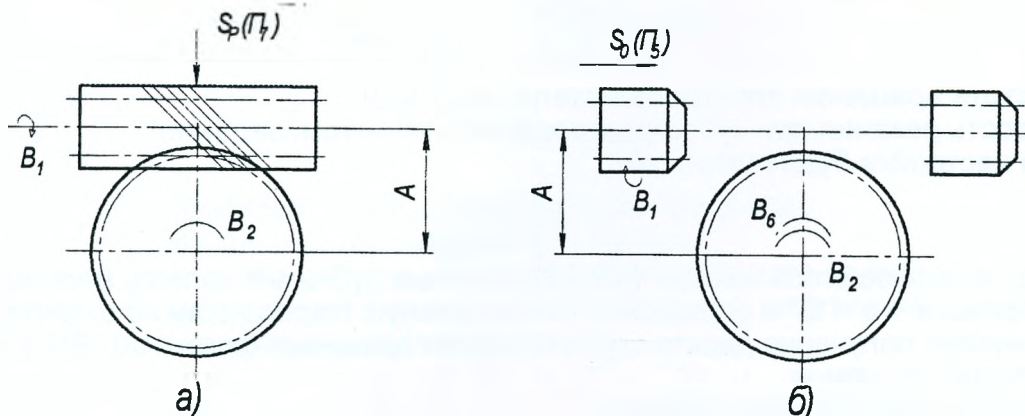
Схемы нарезания зубьев червячных колес:
